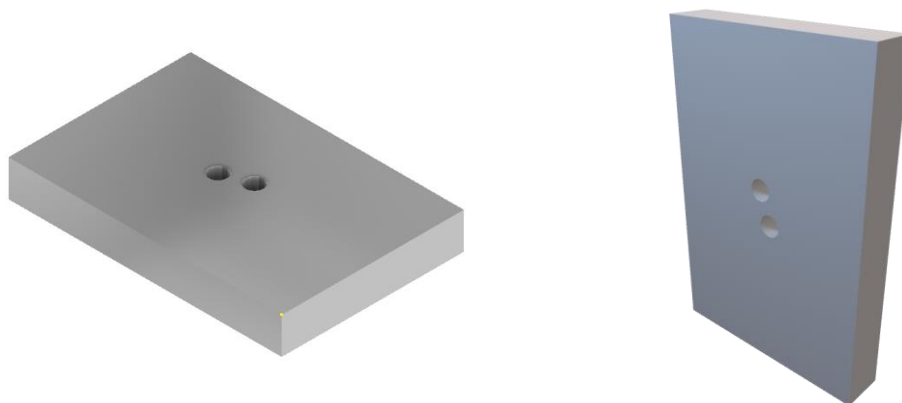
Τρισδιάστατη απεικόνιση αποστολής 13
